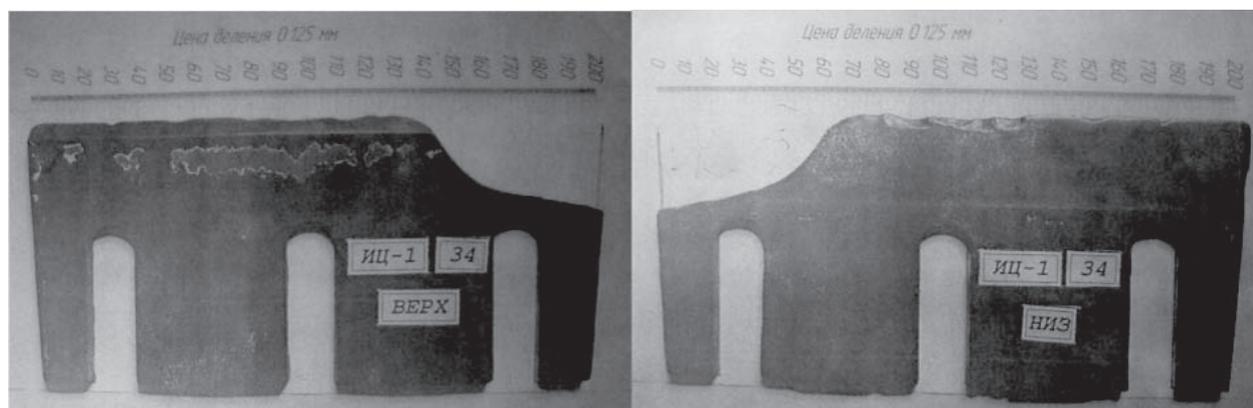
Разрушения ножей, изготовленных из чугуна ВЧТГ, кормоуборочного комбайна КВК-800
